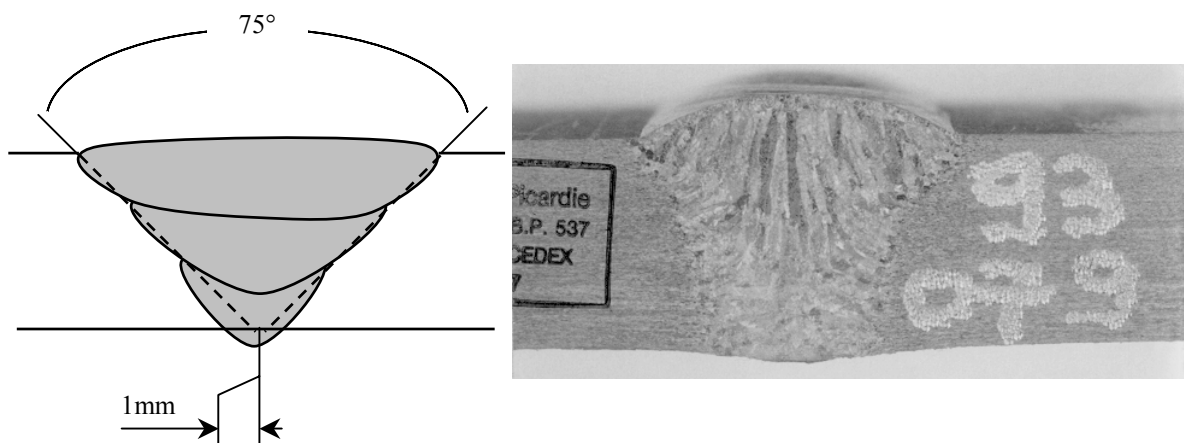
Soudure TIG manuelle sur un tube d'acier duplex (uns 31803 duplex UR 45 N) ϕ 89mm d'épaisseur 5.5mm en 3 passes (talon nul, jeu : 1mm, 230A)
